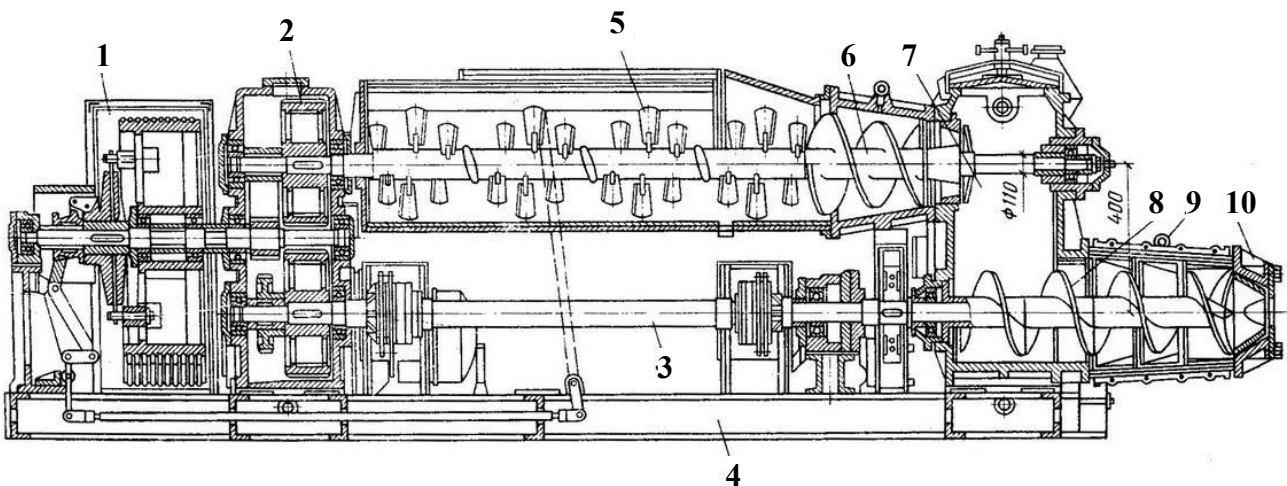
Стрічковий вакуумний комбінований прес: 1,2 – системи передач; 3 – змішувач; 4 – шнек; 5 – вакуум-камера; 6 – шнековий вал; 7 – корпус; 8 – головка преса; 9 – станина; 10 – вал
